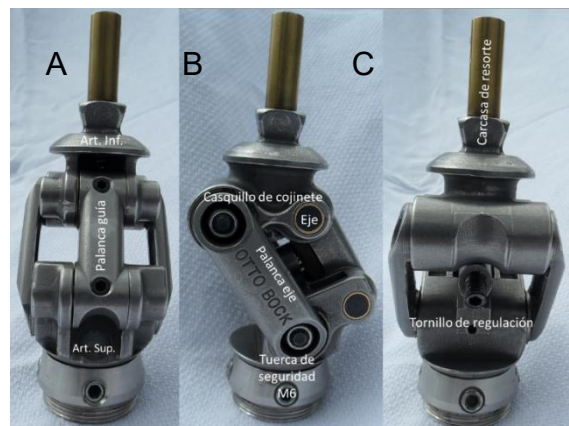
Vista frontal(A), lateral izquierda(B) y posterior(C) de la rodilla policéntrica.
